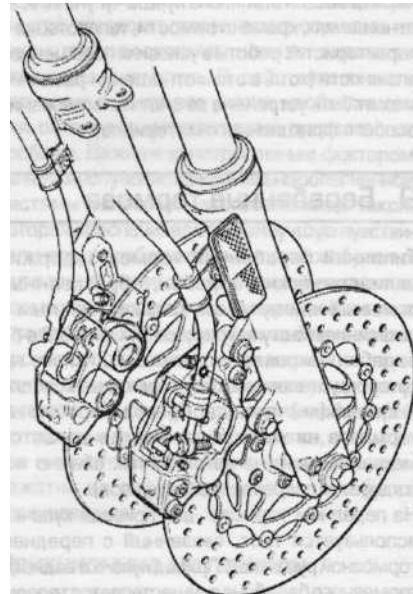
а Тормозной суппорт обхватывает диск и закрепляется на подвижных трубах вилки
